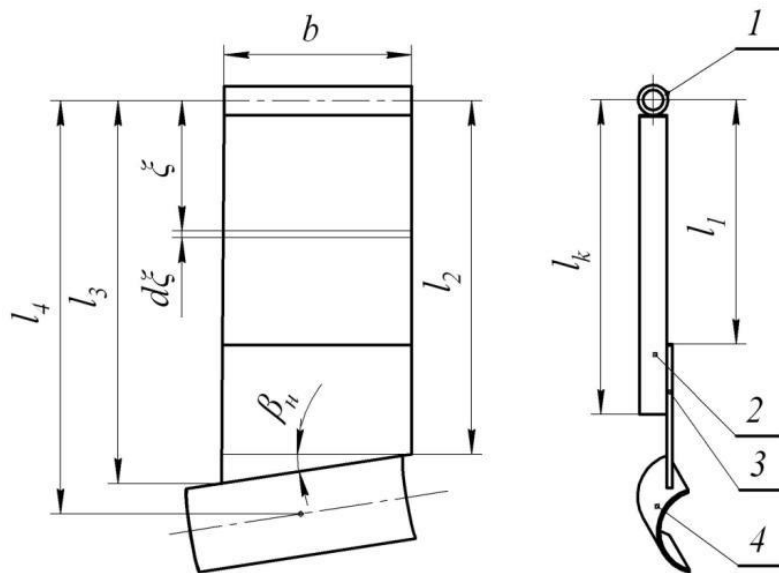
Схема робочого елемента: 1 – шарнір; 2 – копірна частина; 3 – пластина; 4 – ніж
